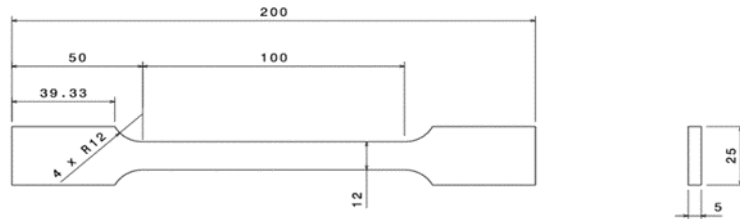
Dimension des éprouvettes de la poutre et de la cornière
